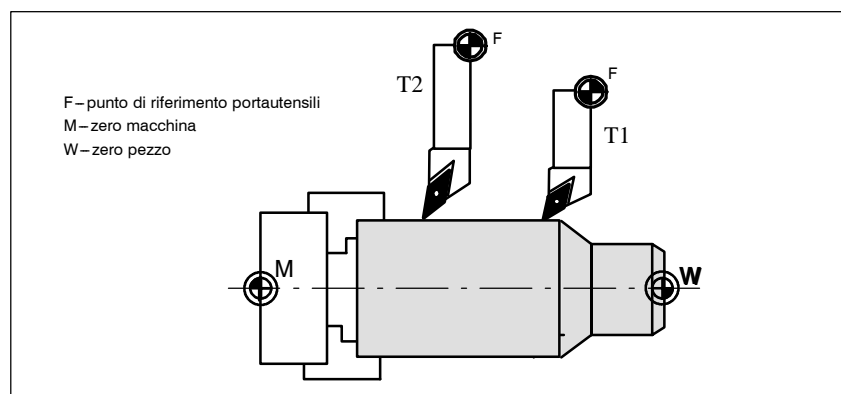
Lavorazione di un pezzo con utensili di dimensioni diverse
